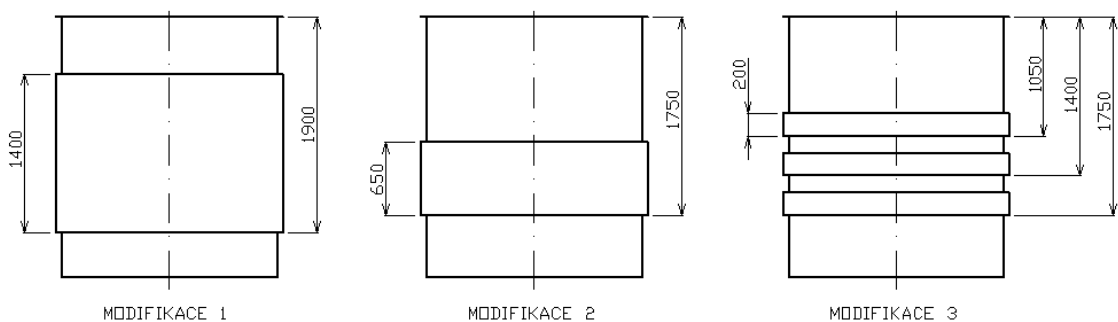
Rozmístění pásů pro základní tloušťku stěny 8 mm
